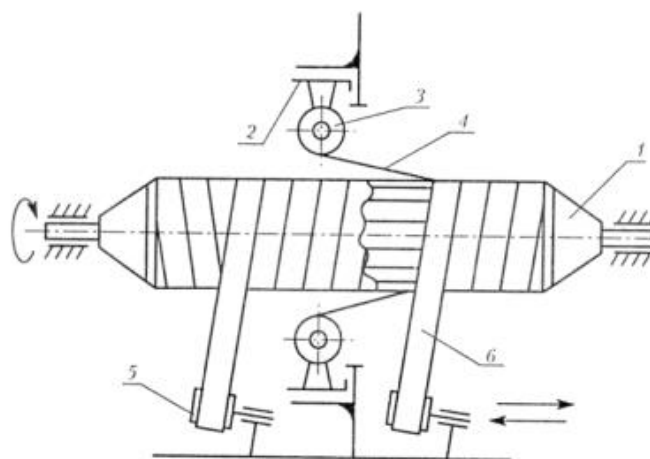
Схема продольно-поперечной намотки: 1 – отправка, 2 – вертлог, 3 – шпули, 4 – ленты продольной укладки, 5 – поперечные раскладчики, 6 – ленты поперечной намотки
